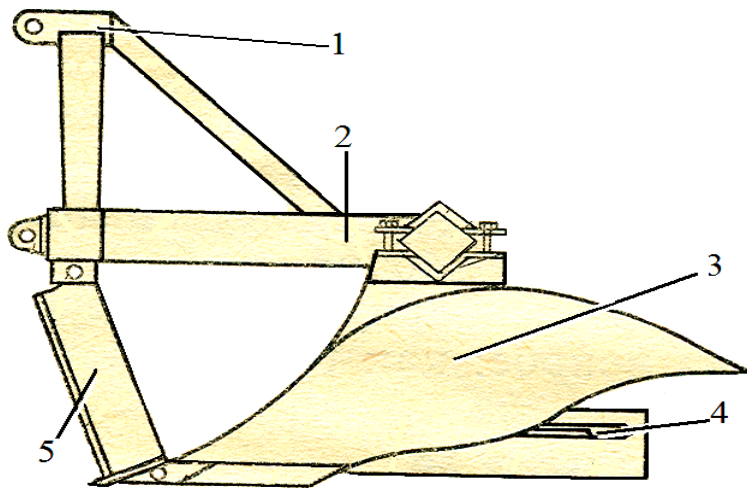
Двокорпусний плуг ПЛ-2-50:
